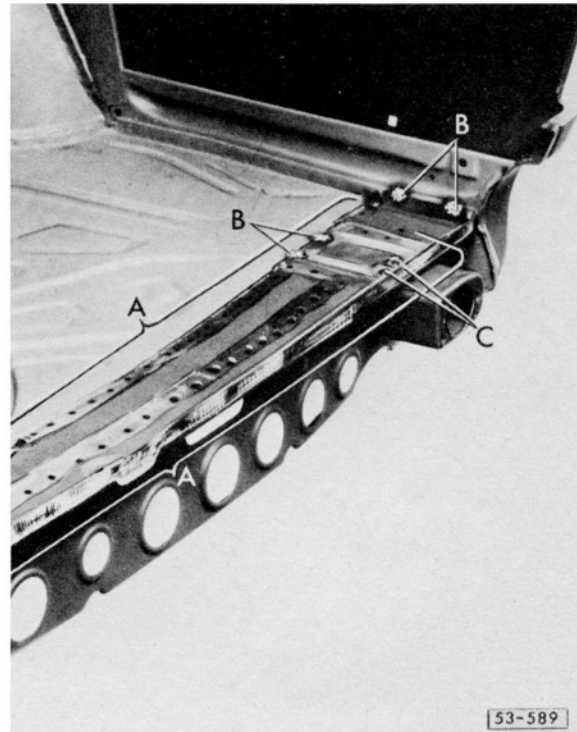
Zwischenstück und Querträger am Abschlußblech einschweißen.
